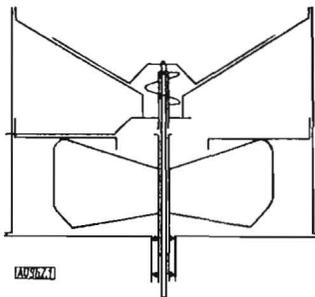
Schema des Speisers für die Bestäubungsmaschine TN-3
